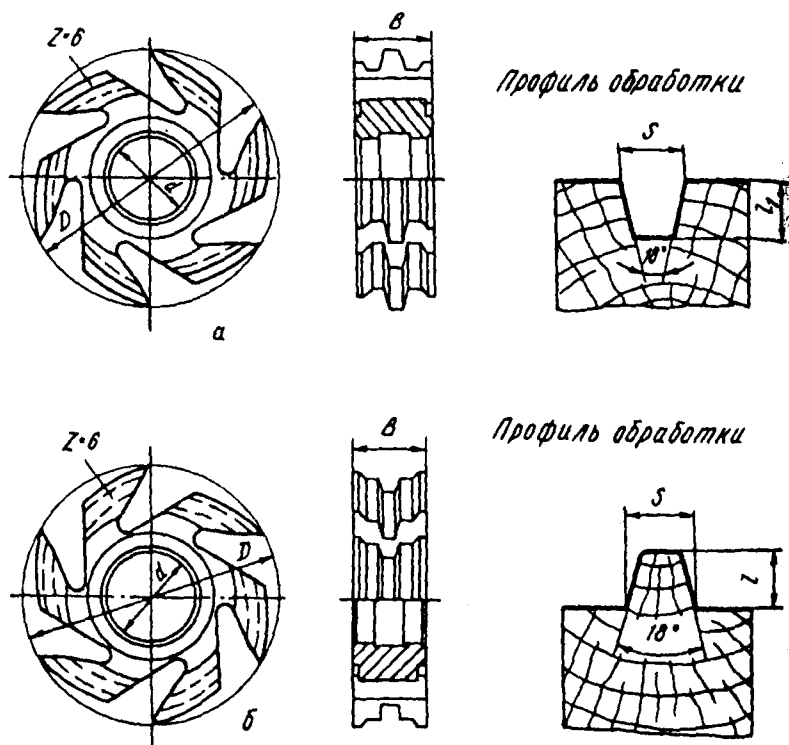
Фрезы для обработки пазов и гребней соединения К-5:
